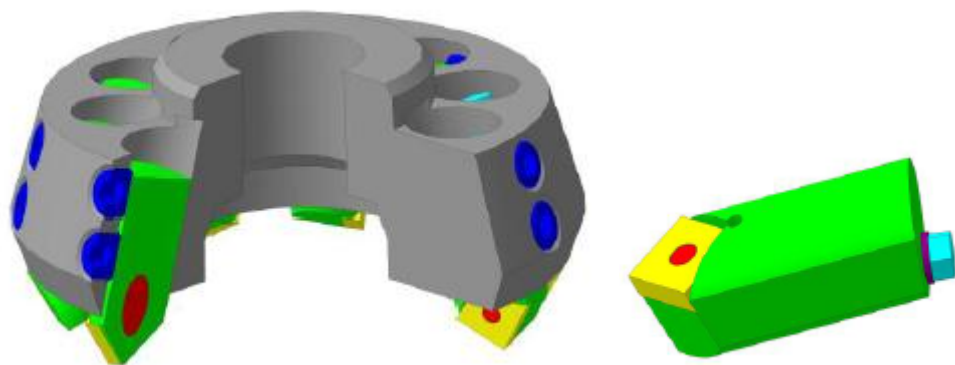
Розріз торцевої фрези і циліндрична ріжуча вставка, що містить чотиригранну твердосплавну пластину (3D-модель)
